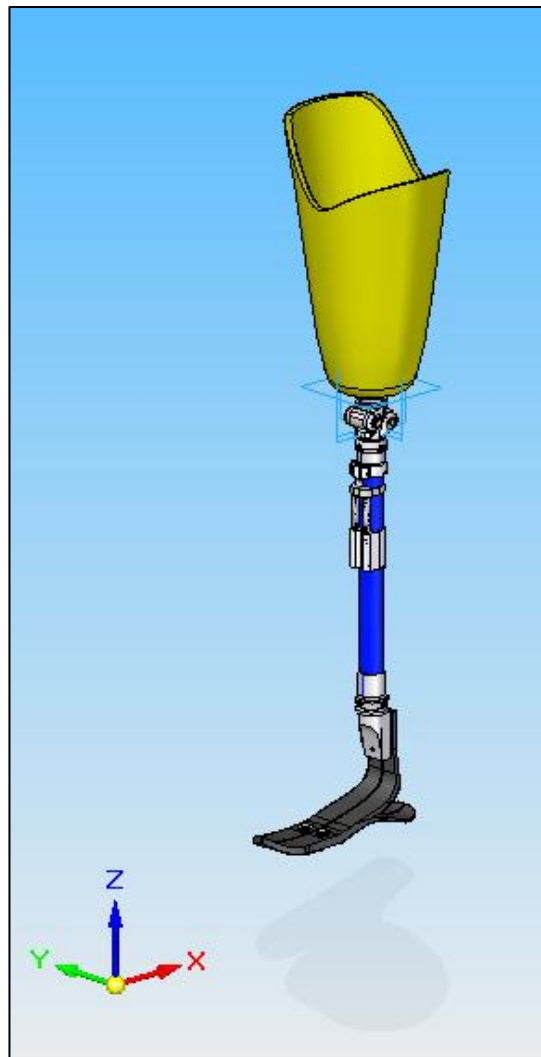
Vista del conjunto pie-tobillo. Solid Edge.
